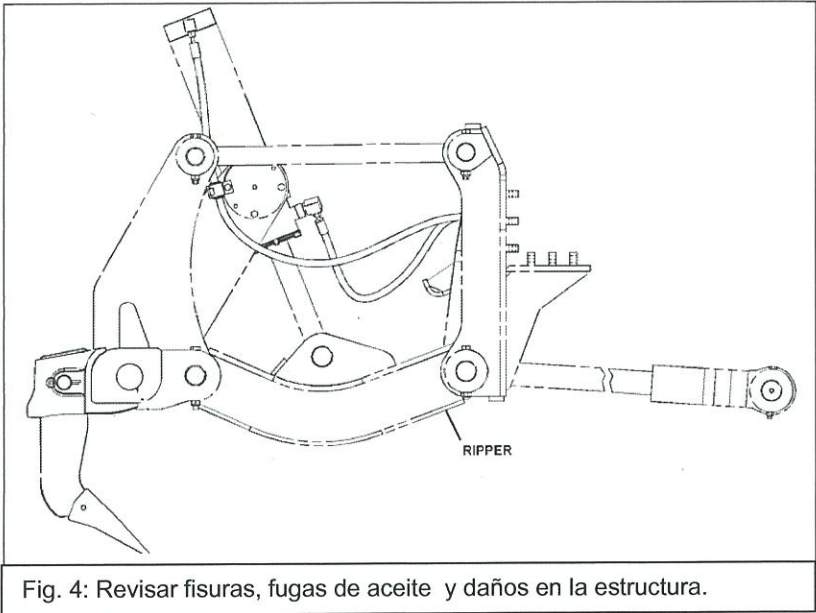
Revisar fisuras, fugas de aceite y daños en la estructura.
